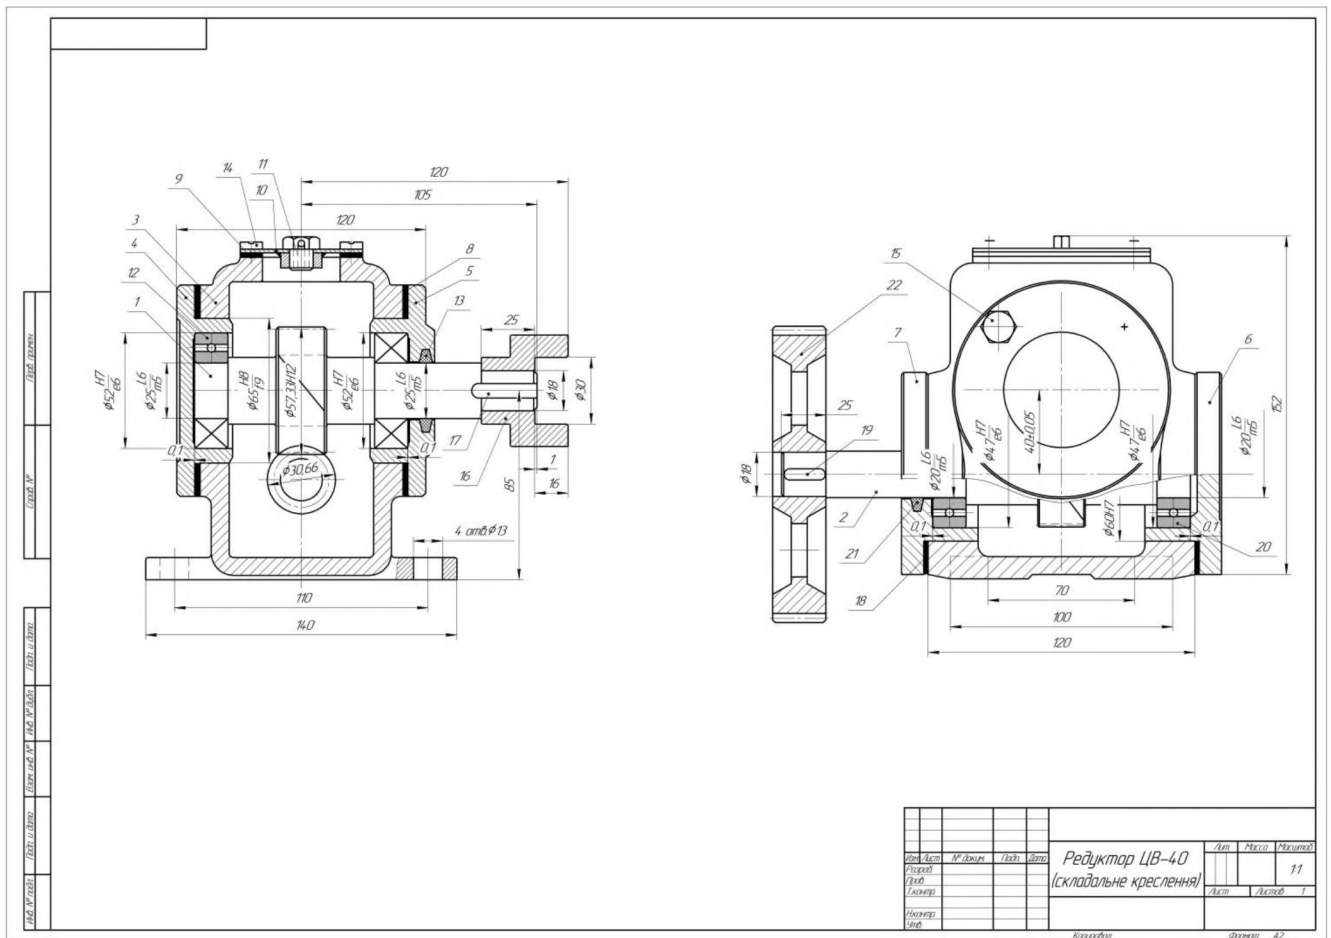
Складальне креслення редуктора ЦВ-40
